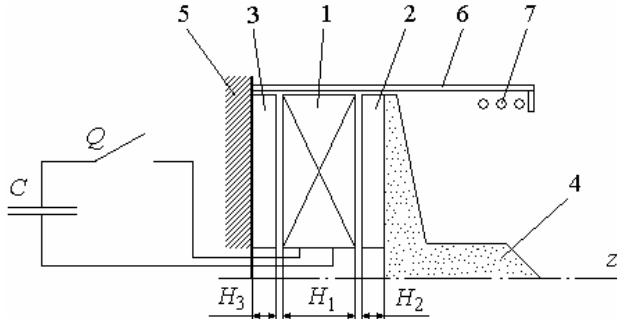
Конструктивная схема ЛИИЭП: 1 – индуктор; 2 – стационарный якорь; 3 – подвижный якорь; 4 – исполнительный элемент; 5 – упор; 6 – корпус; 7 – демпферная пружина
